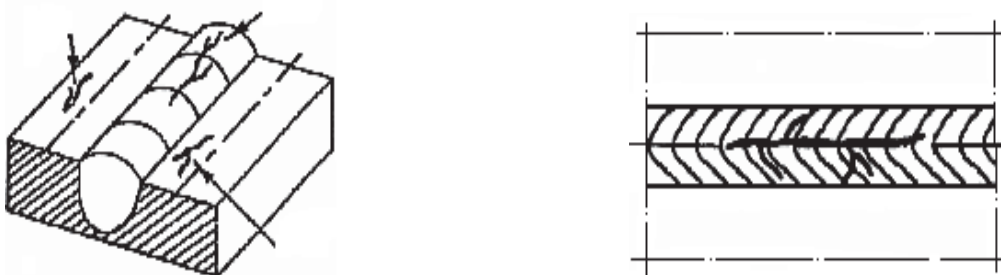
Схематическое изображение разветвленной трещины сварного соединения
